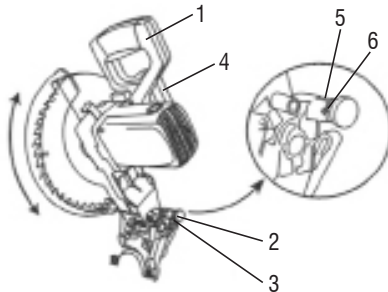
Transporte y almacenaje del cabezote de la máquina
